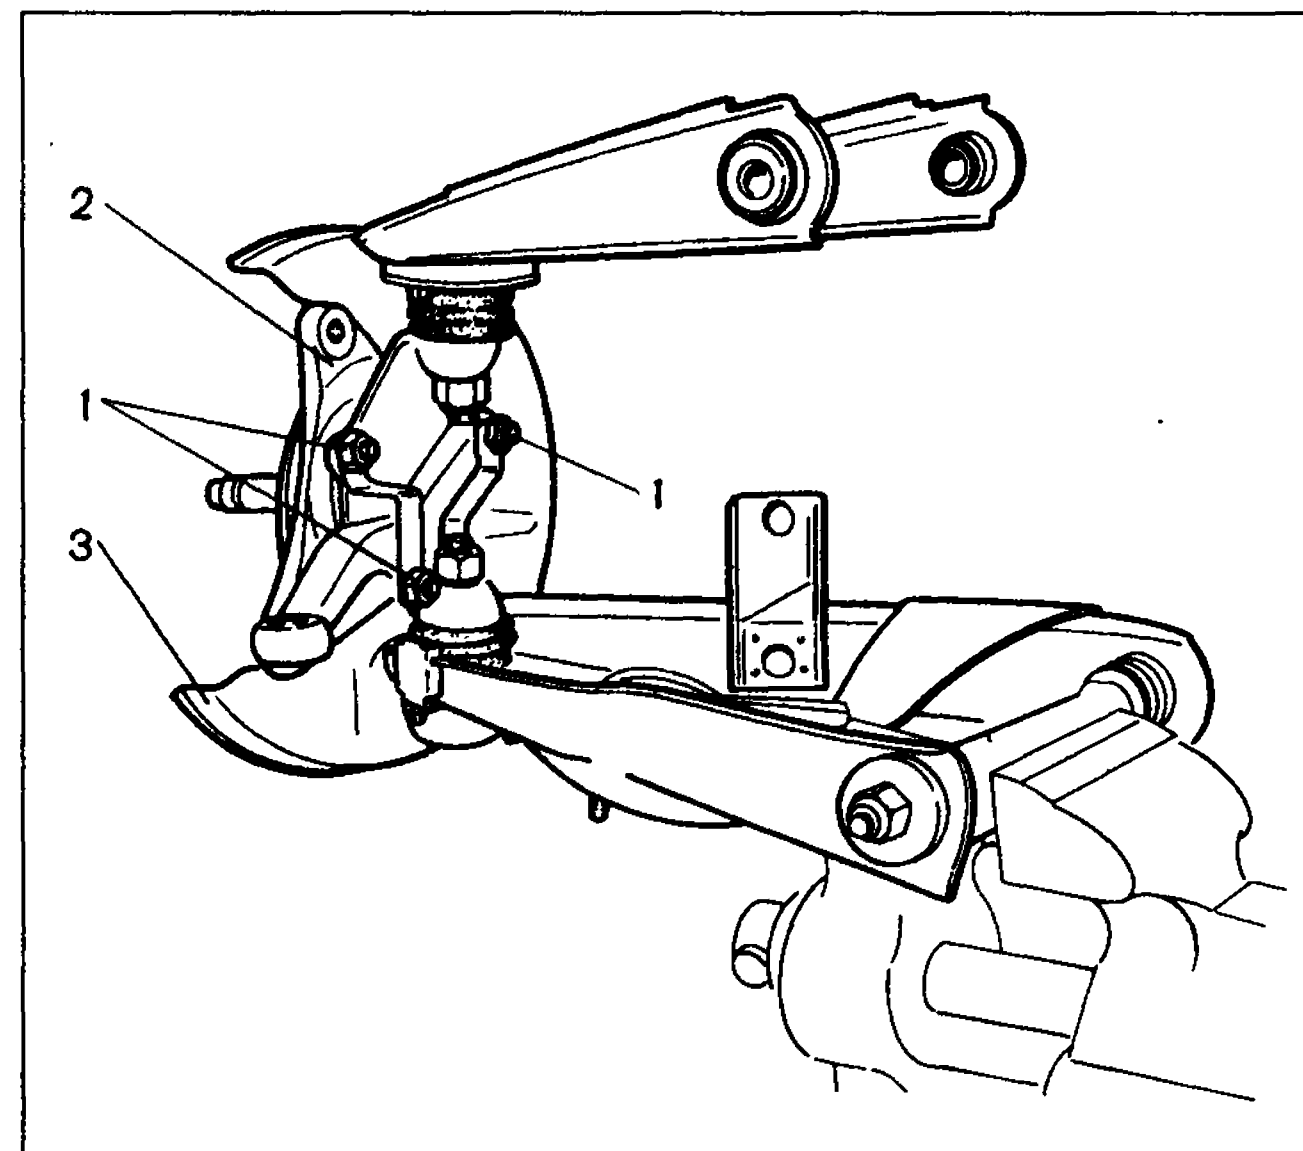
Узел подвески левого колеса, закрепленный на верстаке для разборки:
